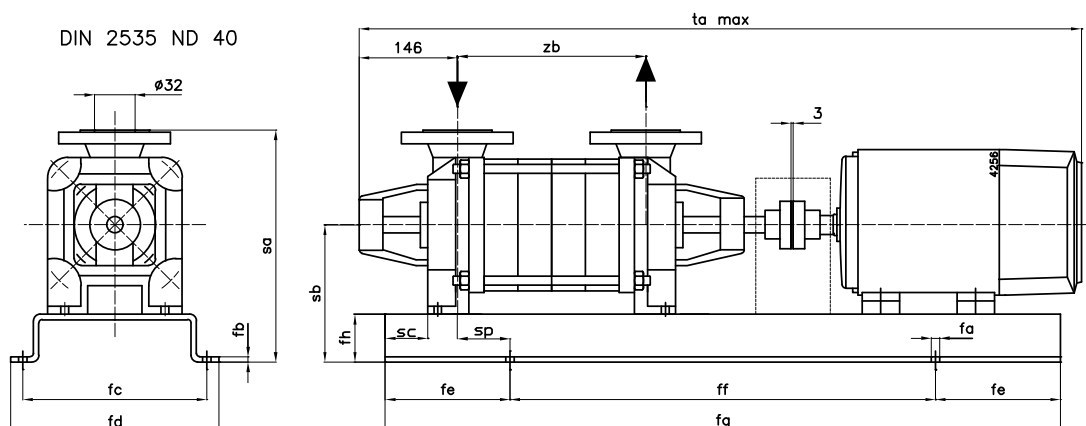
Dimensions ensemble moto-pompe MCH(S)(W) 12,5.
